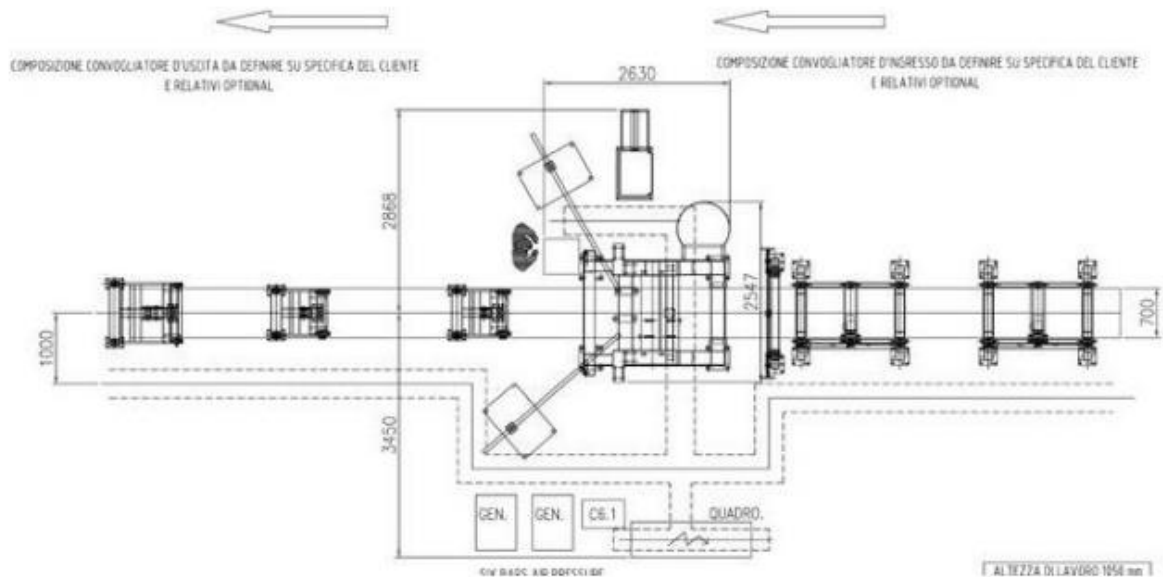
Схема зварювальної установки «Corimrex BWM-TC-1500-500»
